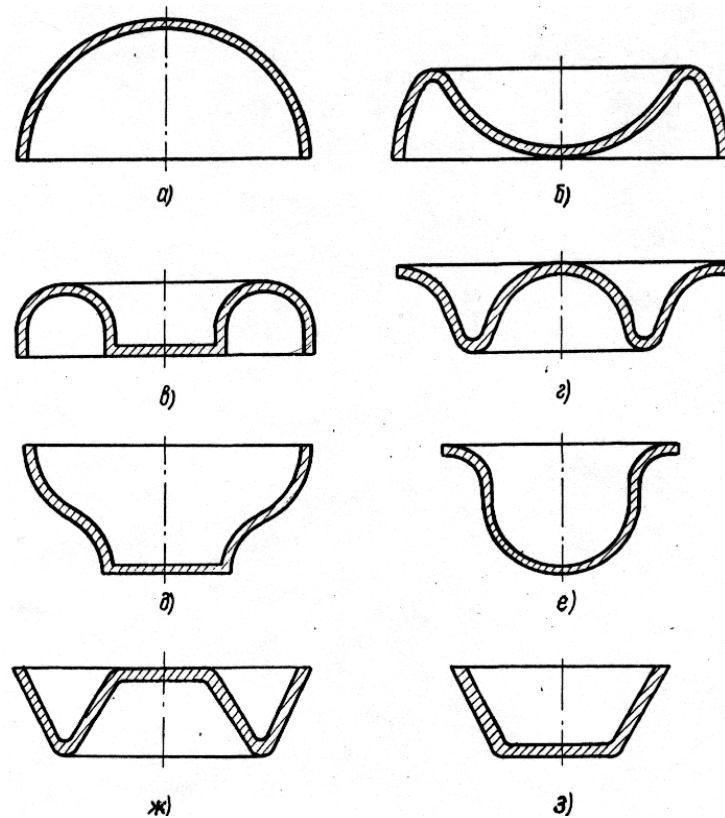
Типовые формы деталей, формобразуемых процессом фрикционно-реверсивной вытяжки эластичной средой по жесткой матрице: а – сферические и сферообразные детали-оболочки; б – детали знакопеременной кривизны, в том числе полуфабрикаты для получения сферообразных оболочковых деталей с равномерной толщиной стенки; в – горообразные детали или полуфабрикаты для получения конусообразных оболочек со знакопеременной образующей (д); г, ж – сложноконтурные полуфабрикаты для получения глубоких сферообразных (е) и конических (з) деталей из плоской заготовки
